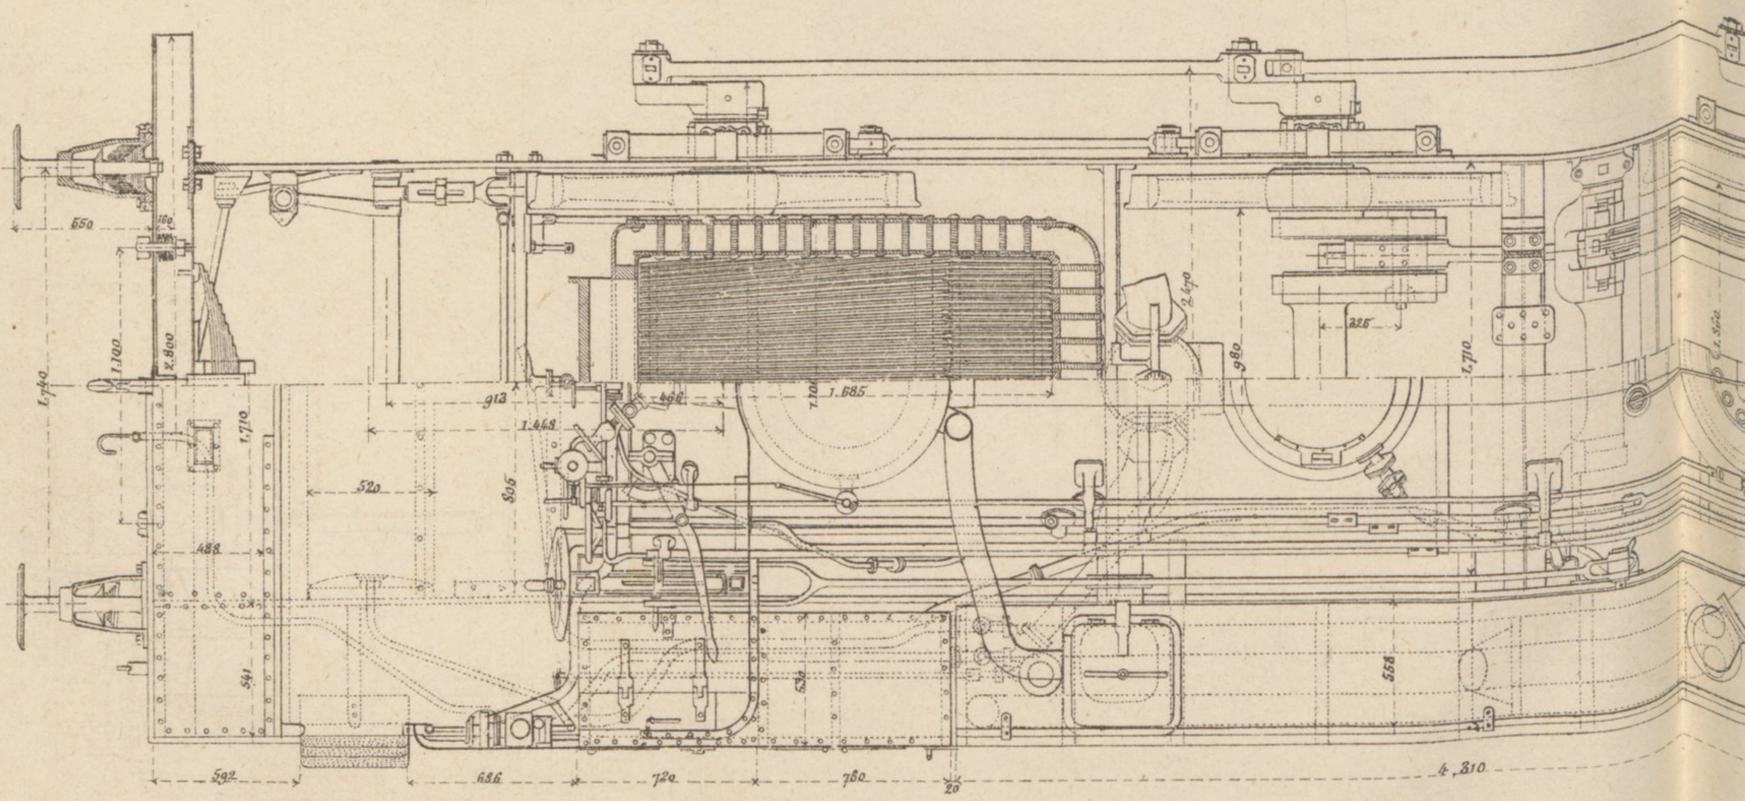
Plan du mécanisme et Coupe par le foyer et les travers
